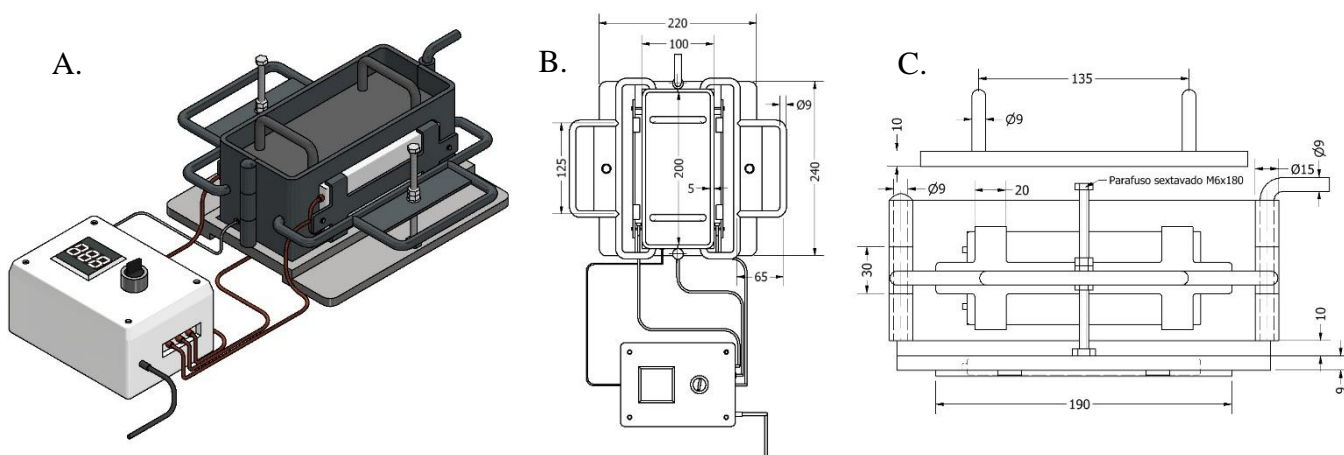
Equipamento pronto para moldagem dos blocos compostos (A), vista superior (B) e vista frontal (C)
